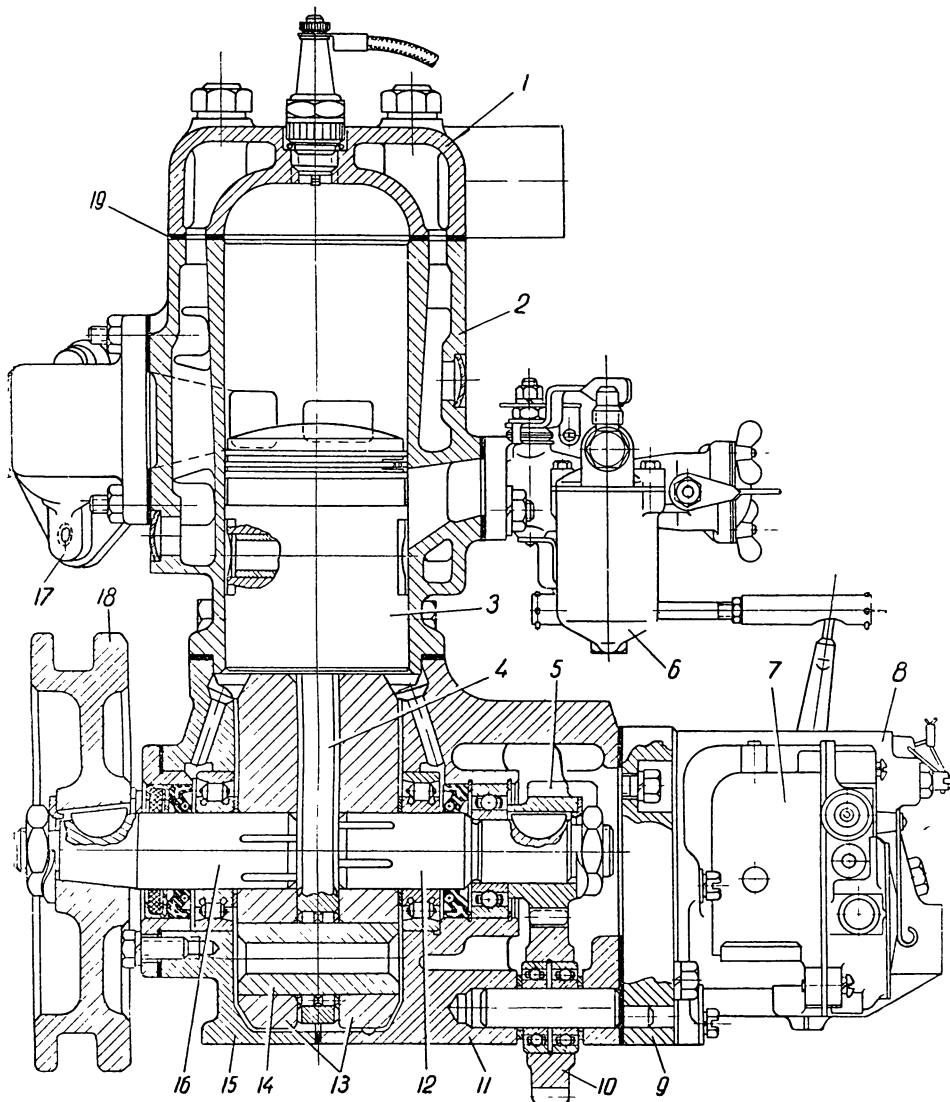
Пусковой двигатель ПД-10М (продольный разрез)
